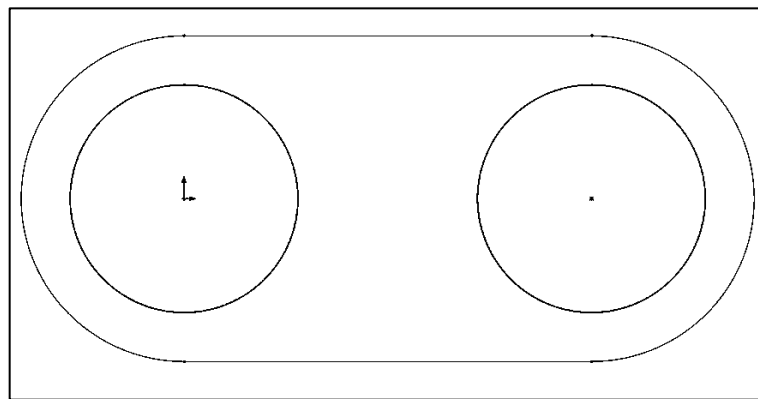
Diseño de doble eje para una máquina ensiladora.
